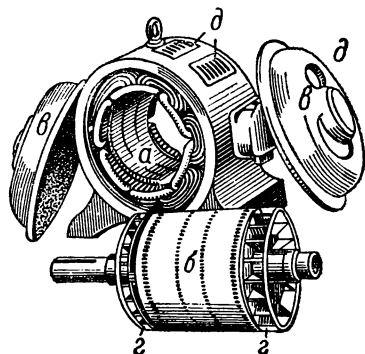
Трехфазный двигатель переменного тока в разобранном виде: а — статор; б — ротор; в — подшипниковые щиты; г — вентиляторы; д — вентиляционные отверстия.
